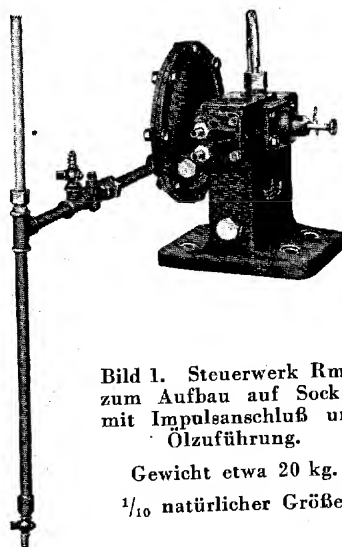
Steuerwerk Rm-e zum Aufbau auf Sockel, mit Impulsanschluß und Ölzuführung.
